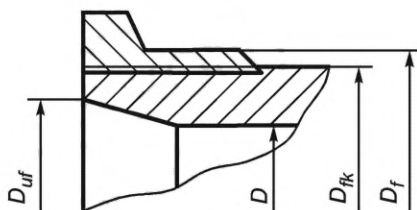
Концевая часть соединяемой детали резьбовая
